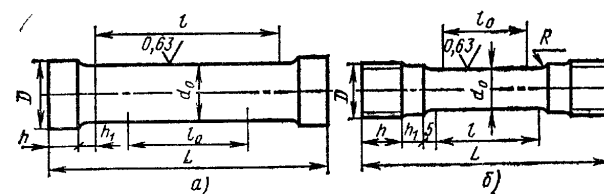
Образцы для испытаний металла шва, металла различных участков околошовной зоны и наплавленного металла на статическое (кратковременное) растяжение:
